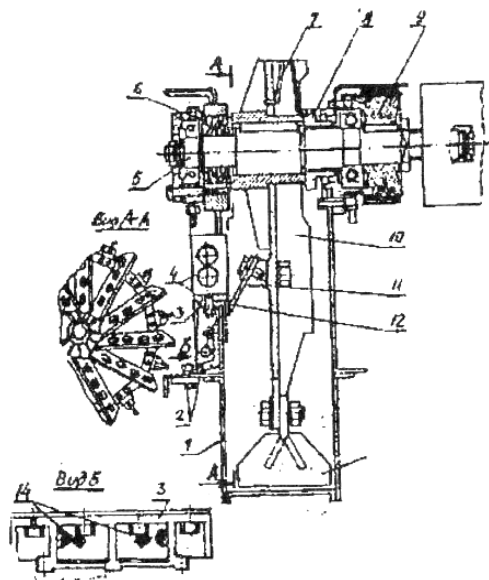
Измельчающий аппарат кормоуборочного комбайна «Полесье-3000»:
